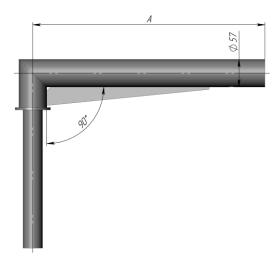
Габаритные и присоединительные размеры кронштейнов исполнений: SA-7-0,5, SA-7-1,0
